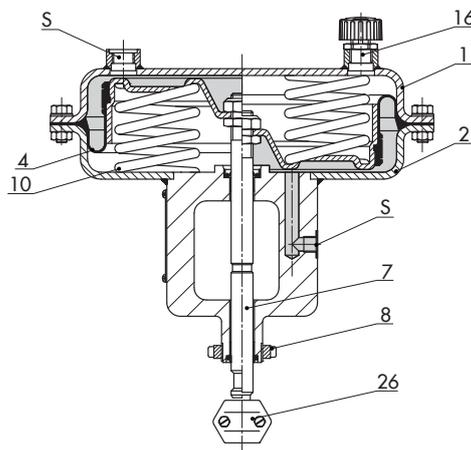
Tipo 3277 para montaje integrado de accesorios (350 cm²)
